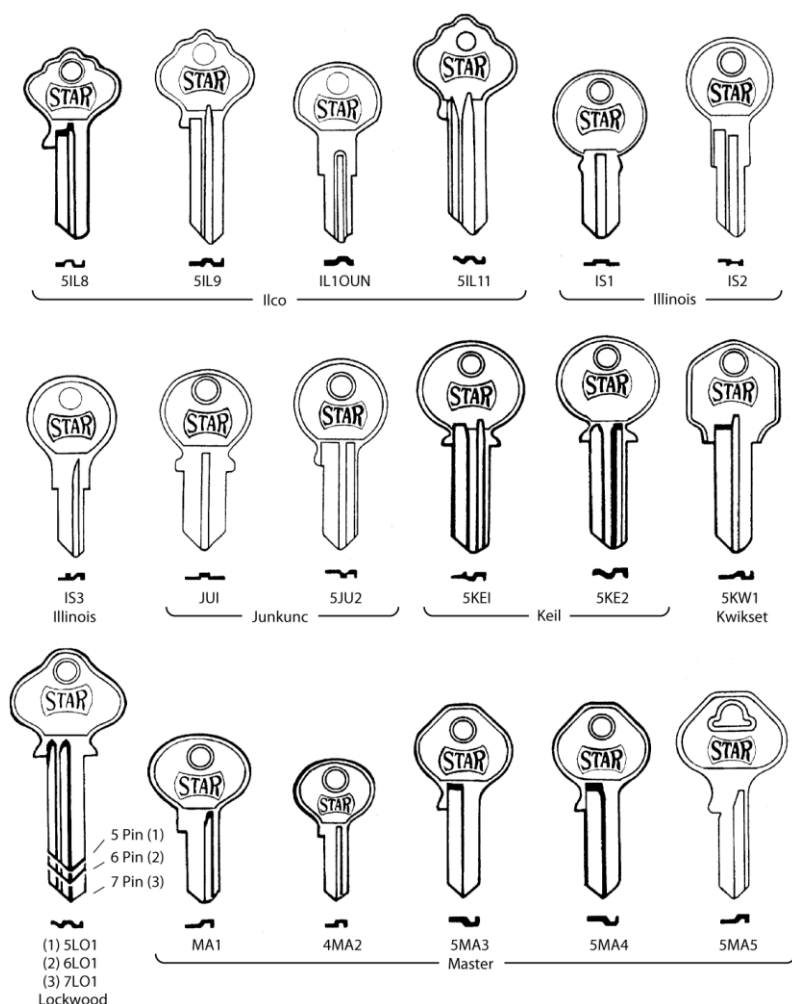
В некоторых справочниках заготовок для ключей приведены их чертежи (С разрешения компании Star Lock и Key Mfg. Co., Inc)
